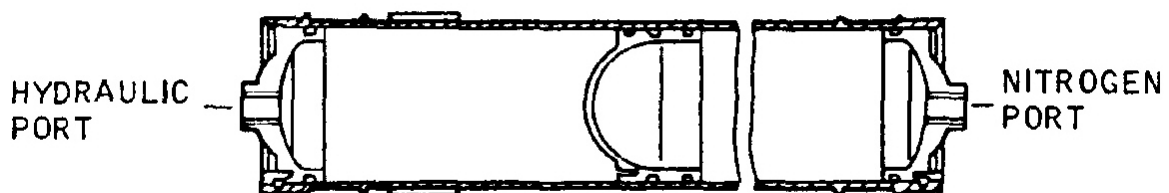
Kolbendruckspeicher (Beispiel: VFW 614)
